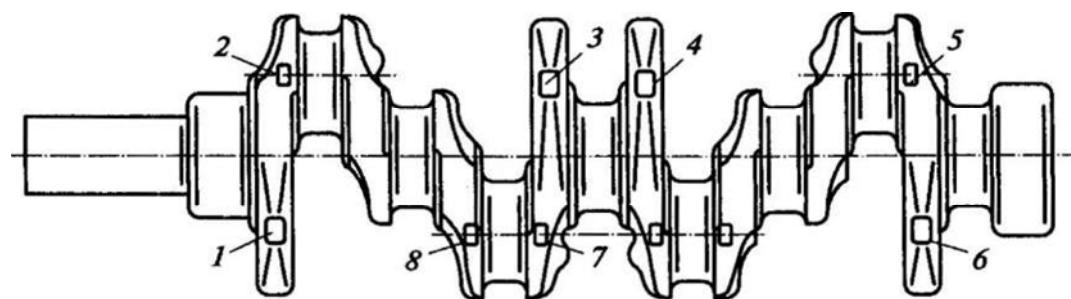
Заготовка коленчатого вала двигателя: 1—8 — опорные технологические площадки
